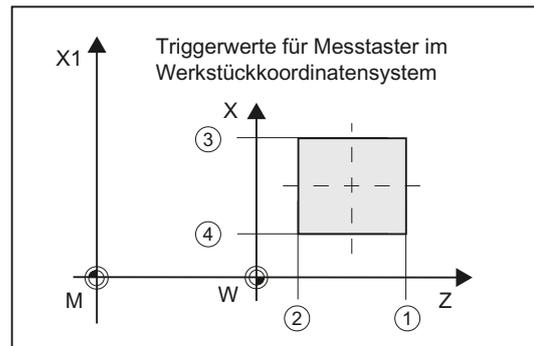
Werkzeugmesstaster, werkstückbezogen (G18)
